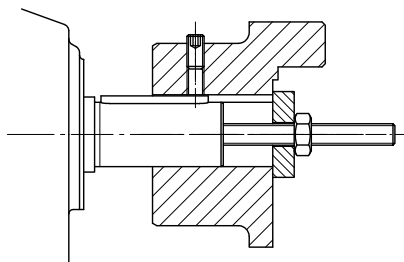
Beispiel einer einfachen Aufziehvorrichtung
